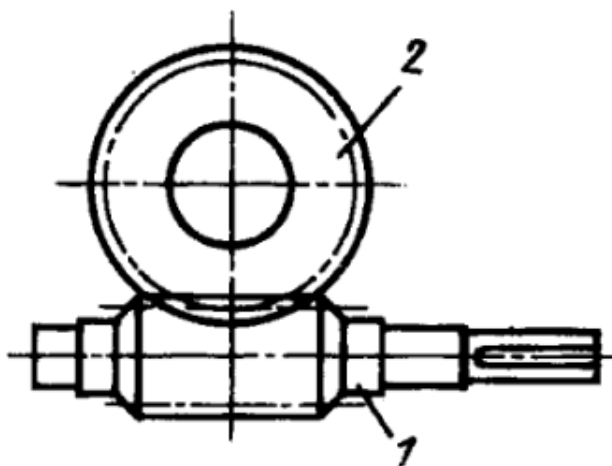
Червячная передача: 1 – червяк; 2 – червячное колесо
